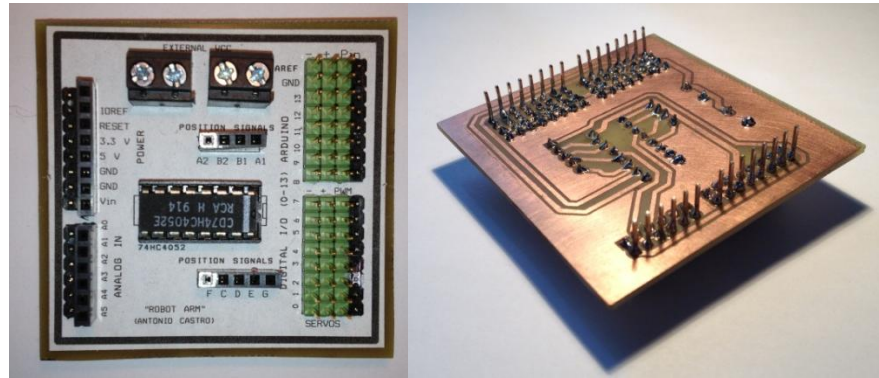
Placa diseñada implementada y completa con componentes soldados
